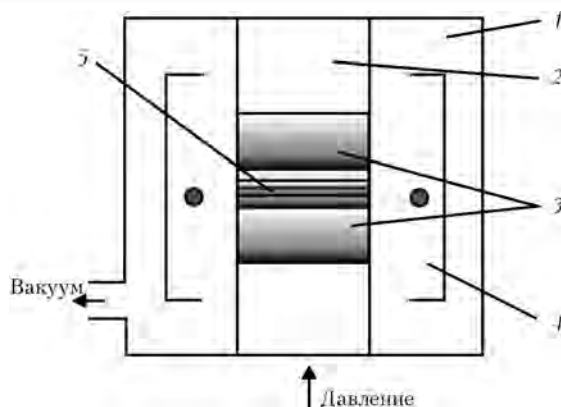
Схема установки диффузионной сварки в вакууме: 1 – вакуумная камера; 2 – прижимной шток; 3 – свариваемые образцы; 4 – электронно-лучевой нагреватель; 5 – фольга Ti/Al
